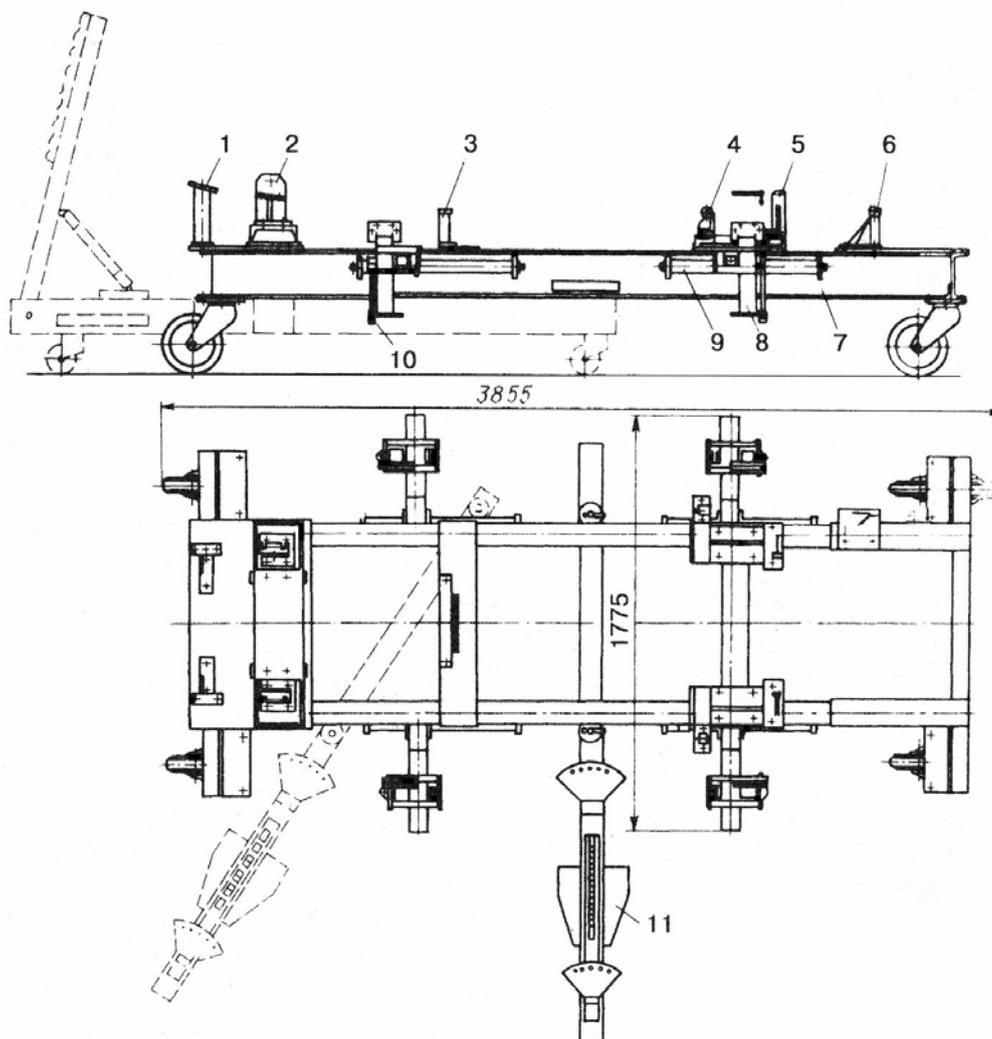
Установка БС-123: 1 – 6 – попарные кронштейны; 7 – рама; 8 – стойка; 9 – эксцентрический вал; 10 – регулировочный винт; 11 – установка БС-124
